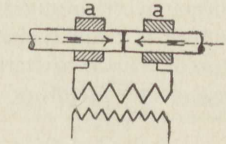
Elektrisches Stumpfschweißen.
